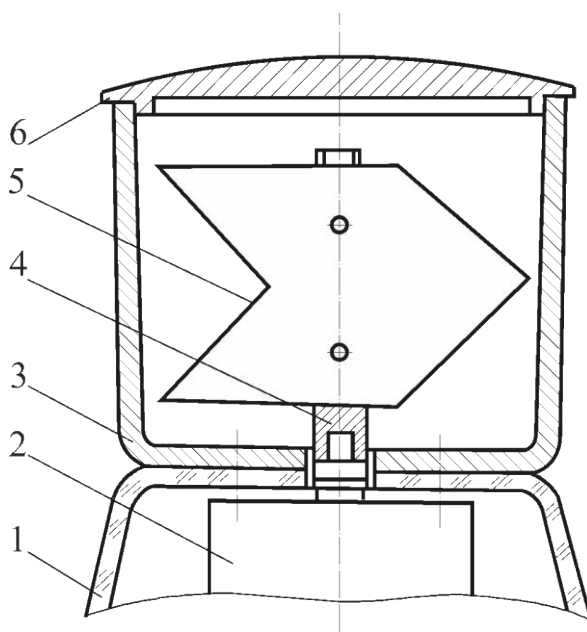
Схема селекционной клеверотерки: 1 – корпус; 2 – электродвигатель; 3 – вертикальный неподвижный барабан; 4 – ротор; 5 – рабочий орган; 6 – крышка
